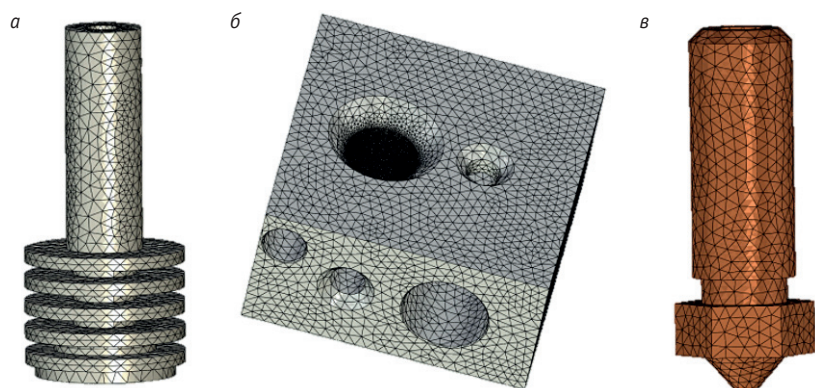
Построение конечно-элементной сетки: а – направляющая с радиатором; б – нагревательный блок; в – сопло
